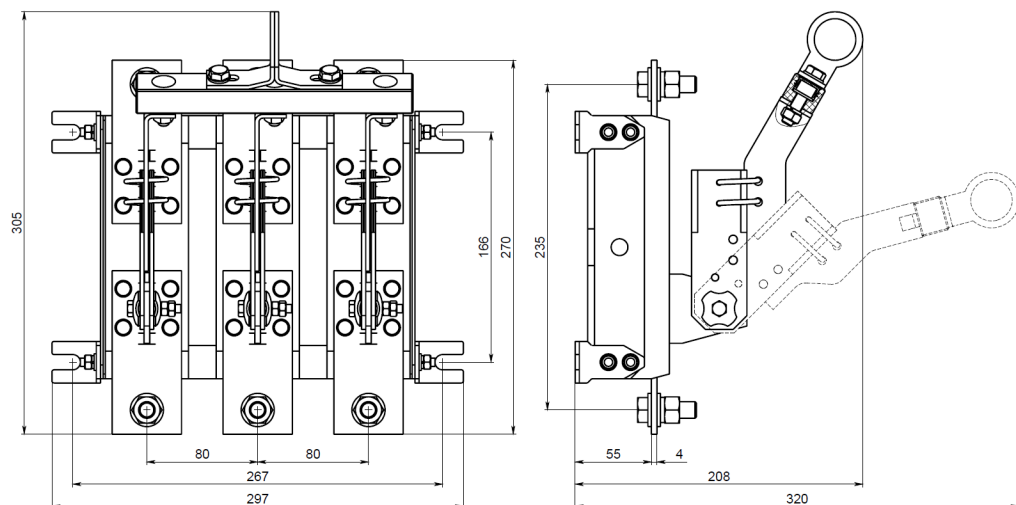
Разъединитель РЕ19-39-31120-00 УХЛЗ с боковой рукояткой, масса 6,4 кг
